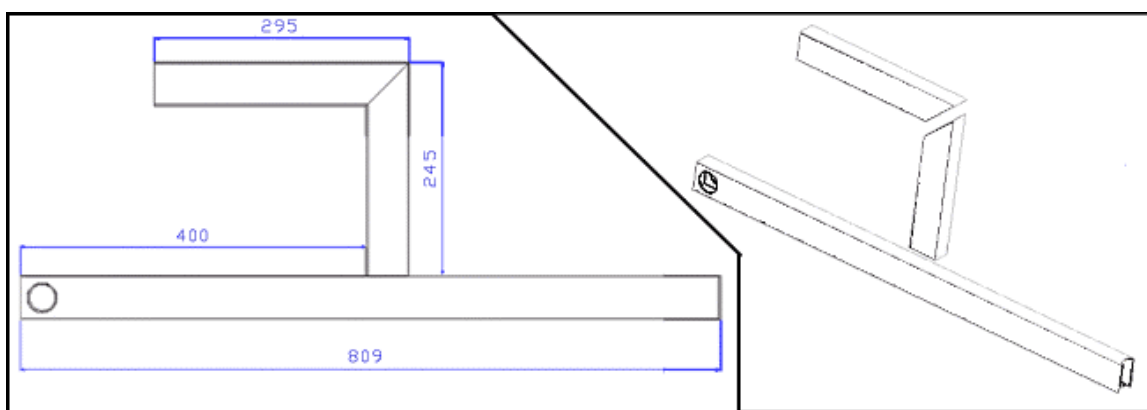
Medidas para a montagem e posterior soldagem do metalon.
